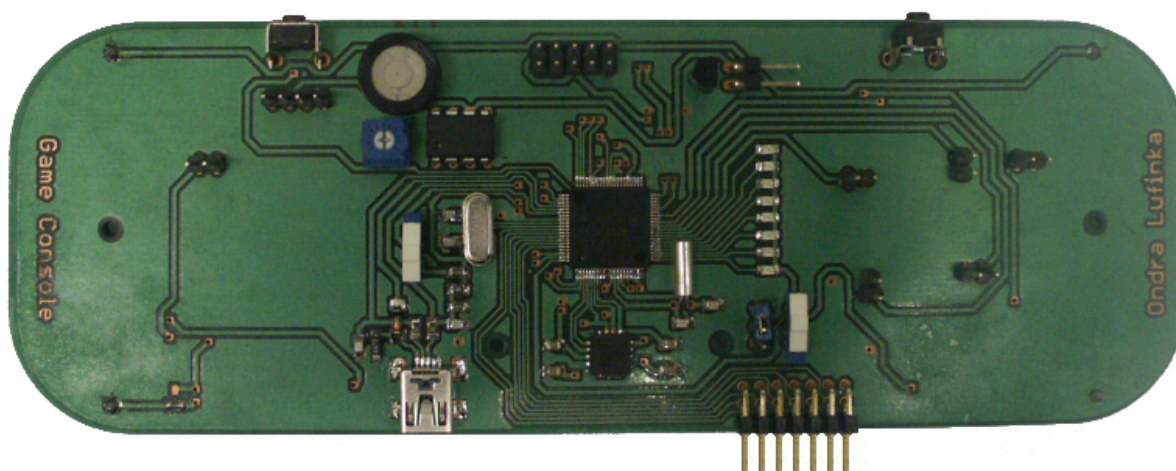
Horní potisk horní desky plošných spojů herní platformy.
